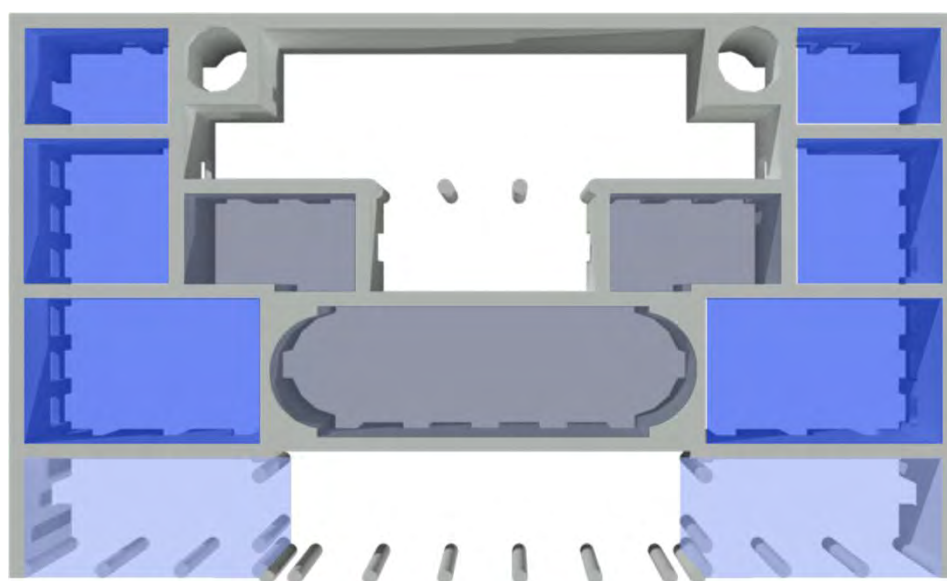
Individuazione della posizione del piano tridimensionale prospettico
